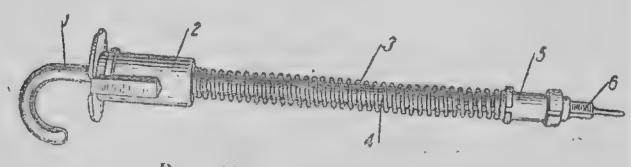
Ударный механизм: 1-крючок; 2-соединительная муфта; 3-боевая пружина; 4-ограничительная трубка; 5-муфта бойка; 6-боек
